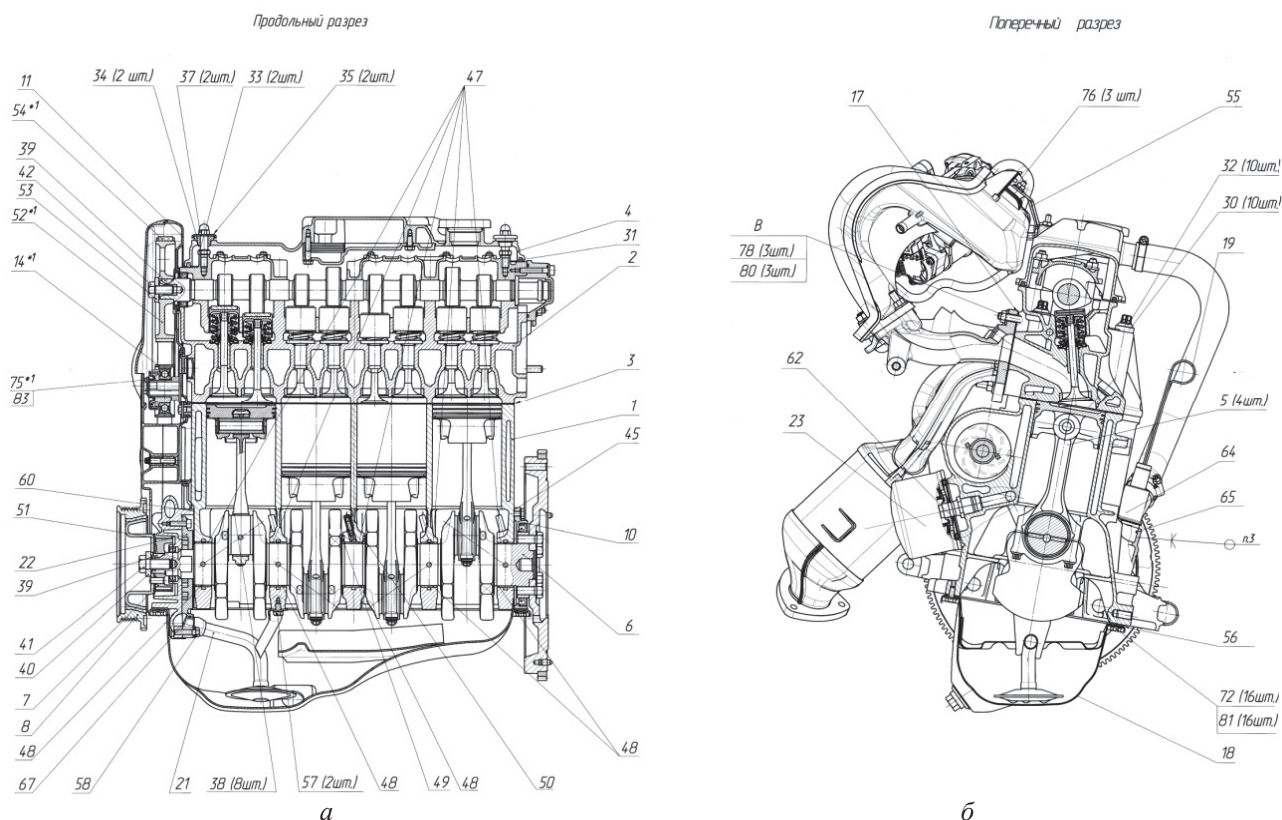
Продольный (а) и поперечный (б) разрезы двигателя ВАЗ – 21116
